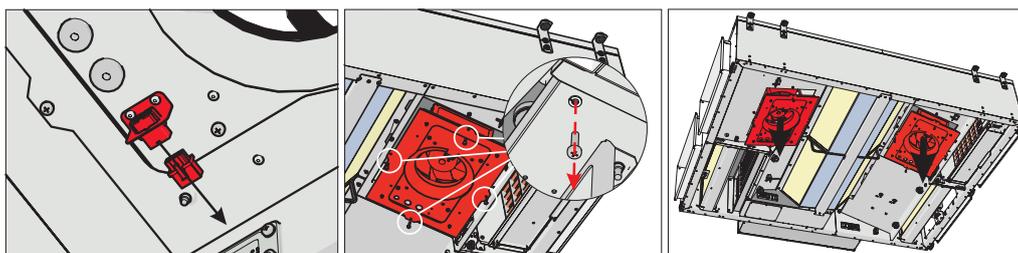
La version en installation au plafond d'AmberAir Compact 1 CX P
